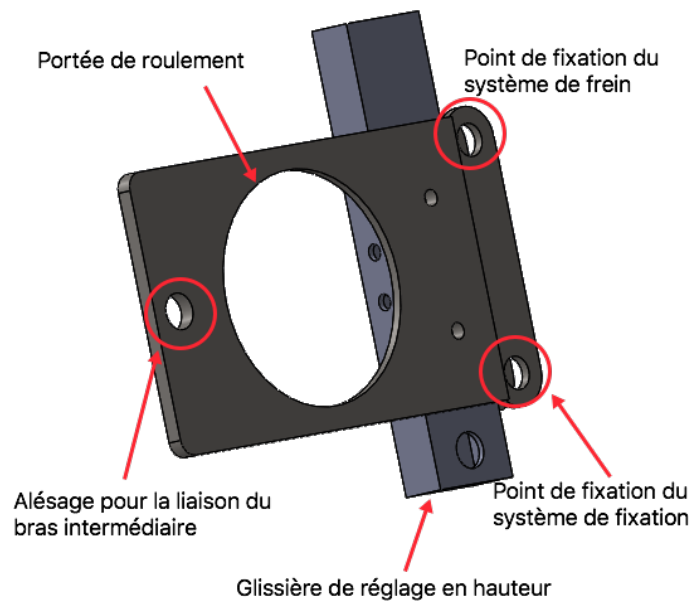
Plaque de fixation à la première roue de friction
